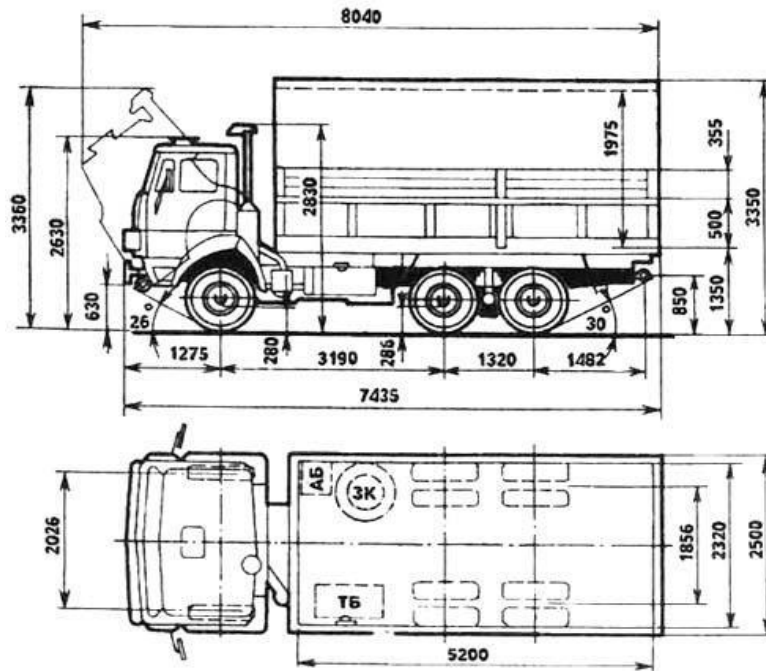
Габаритные размеры автомобиля КамАЗ 5320 (8т)
